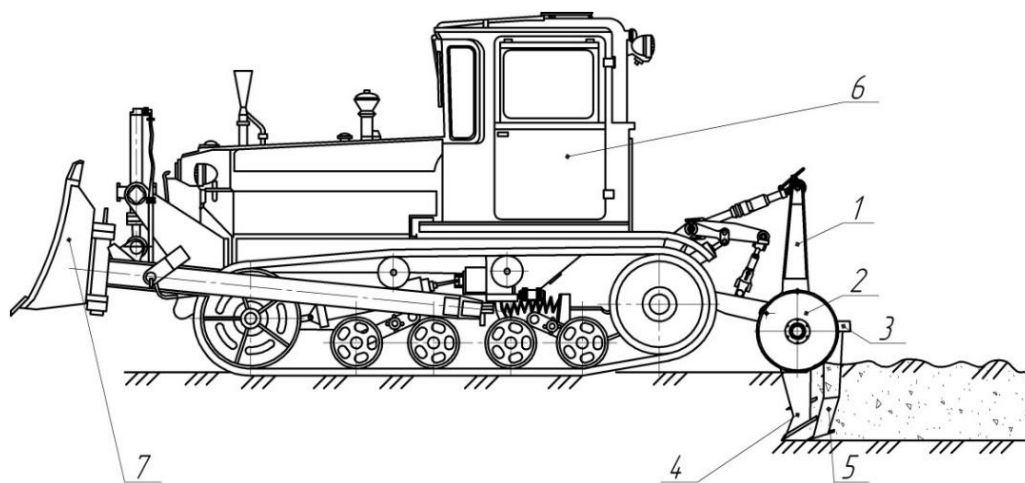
Общий вид глубокорыхлителя (вид сбоку) в рабочем положении.
